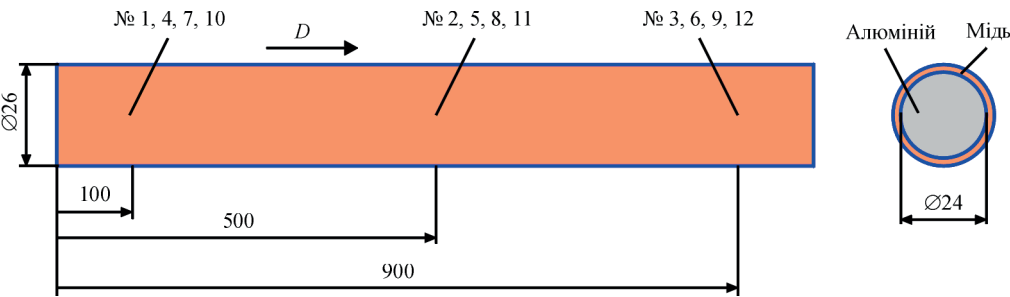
Схема вирізання шліфів з біметалічного стрижня
